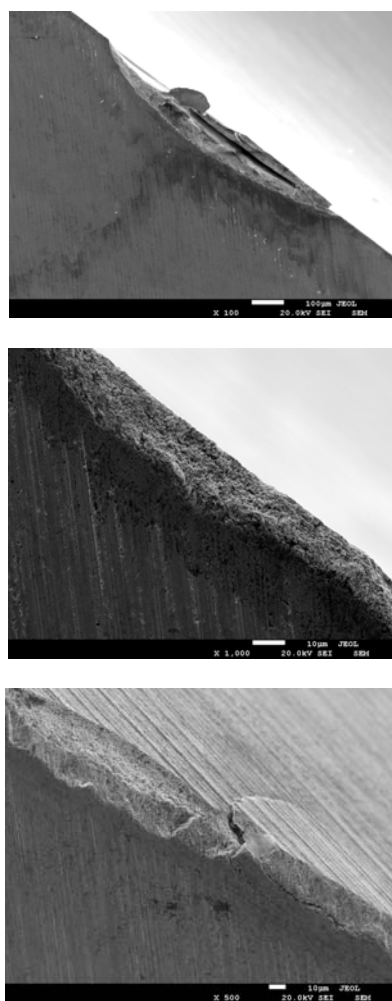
Дефекты режущей кромки твёрдосплавного инструмента, полученные на стадии изготовления
